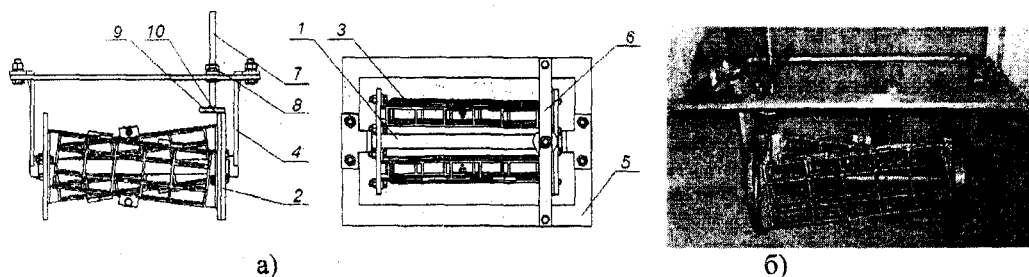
Конструкция опытного приспособления: а) 1-вал; 2-диск; 3-отсек решетчатый; 4-стойка; 5-рама; 6-штанга; 7-винт 8-гайка; 9-башимак; 10- прокладка; б) общий вид
